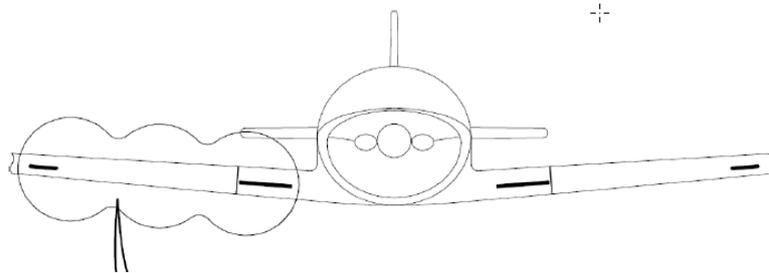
plan d'installation des *stall-strips* (Source : Aerospool)
